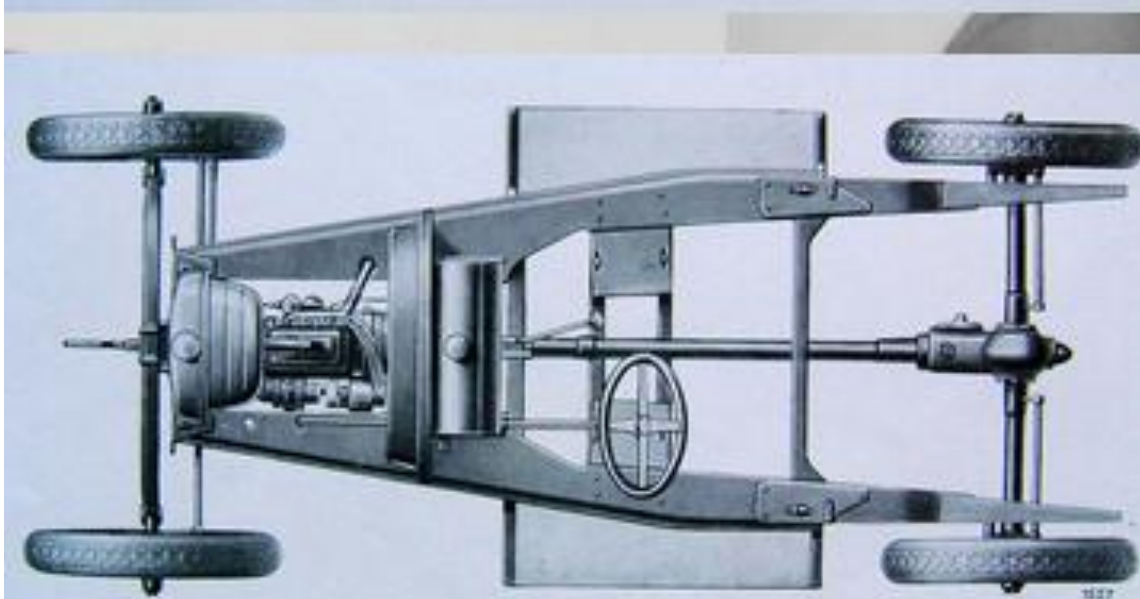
VUE EN PLAN DU CHASSIS 5 CH, TYPE 172-M 2.
